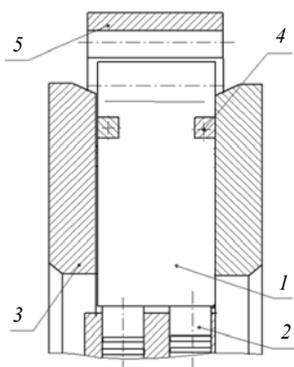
Конструкция передачи с гибким элементом в виде пружинных колец: 1 – плунжер; 2 – поршень волнообразователя; 3 – сепаратор; 4 – пружинное кольцо; 5 – зубчатое колесо
